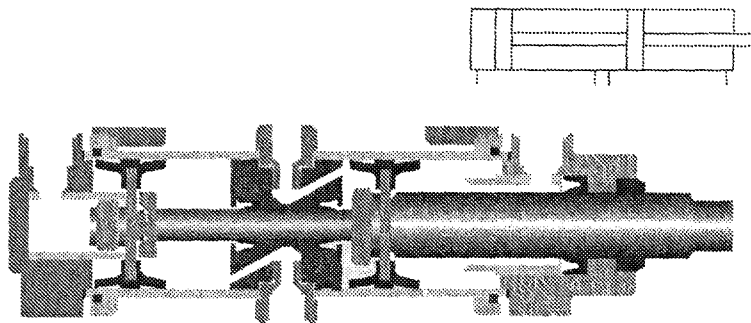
Pohľad na dvojčinný lineárny pneumatický motor
